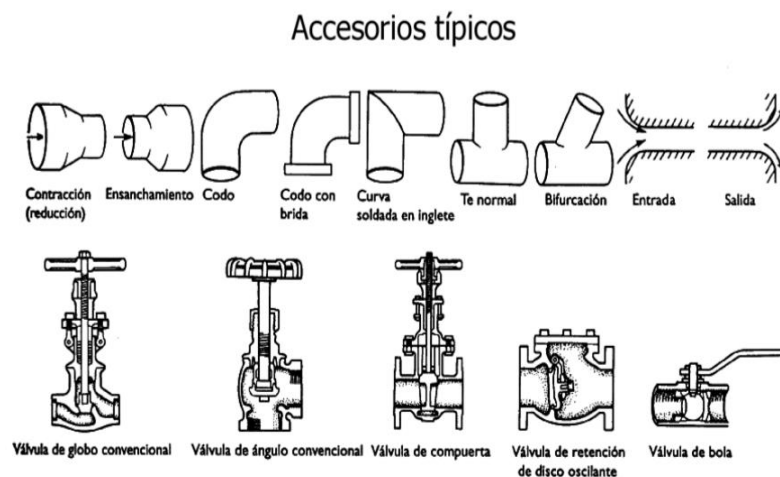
Tipos de elementos donde hay pérdidas menores.
